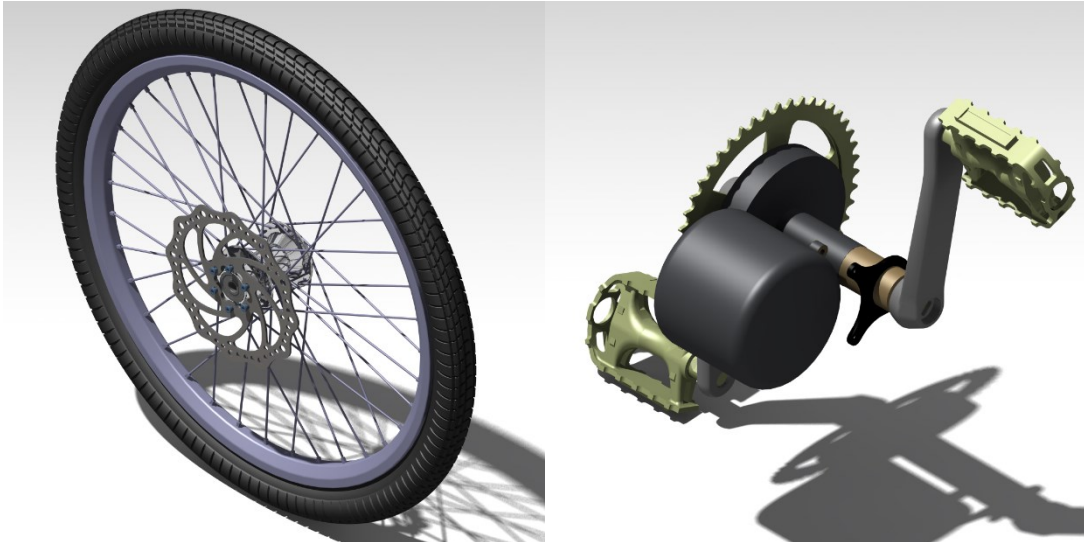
Montagem das rodas e do Bafang. Fonte: Elaborado pelo autor em conjunto com a equipe de CAD / Ergonomia
